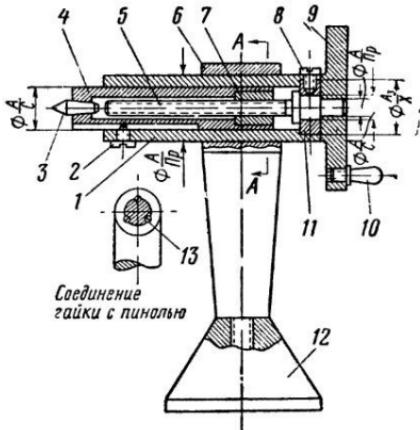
Модель задней бабки токарного станка (схема соединения деталей): 1 — консоль; 2 — стопорный винт; 3 — центр; 4 — пиноль; 5 — винт; 6 — стойка; 7 — гайка; 8 — стопорный винт; 9 — диск; 10 — ручка; 11 — втулка; 12 — основание; 13 — шпонка.
